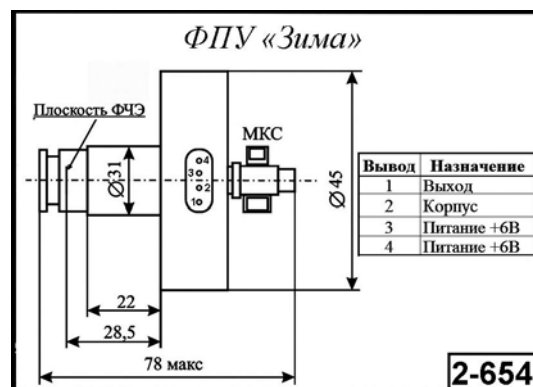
Внешний вид и габаритные размеры ФПУ «Зима»
